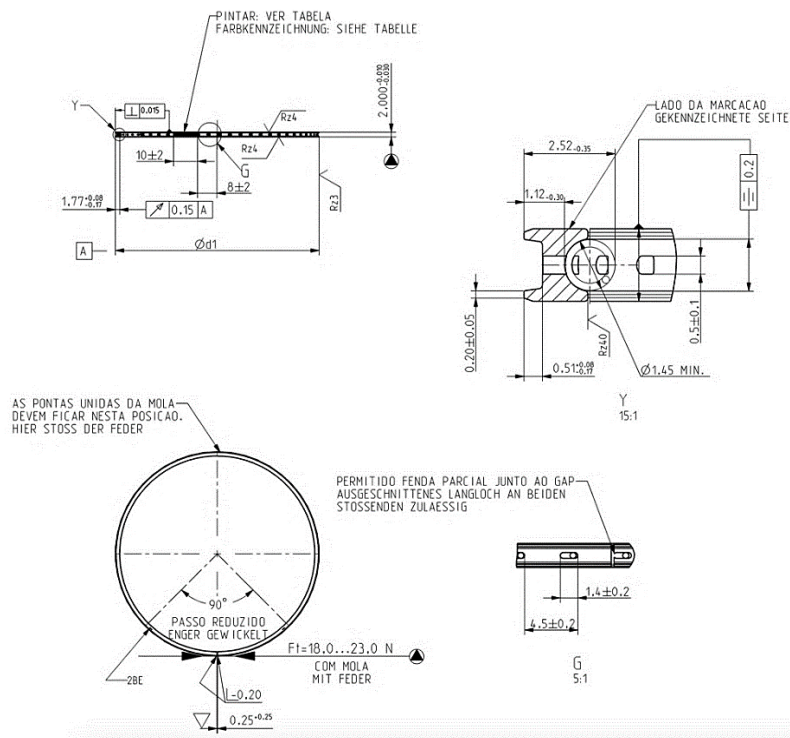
Recorte do desenho técnico do tipo de anel *I-Shaped* em estudo [3].
